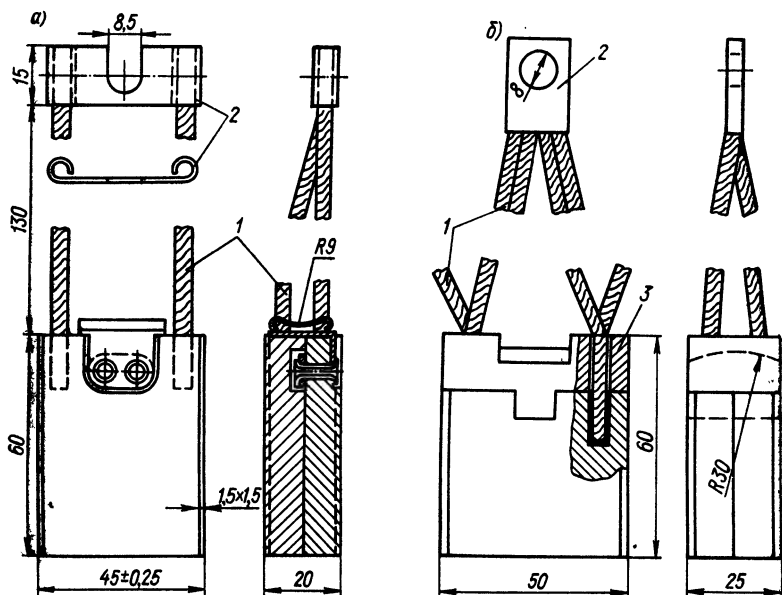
Разрезные щетки: а — с общей нажимной шапочкой; б — с резиновым амортизатором
